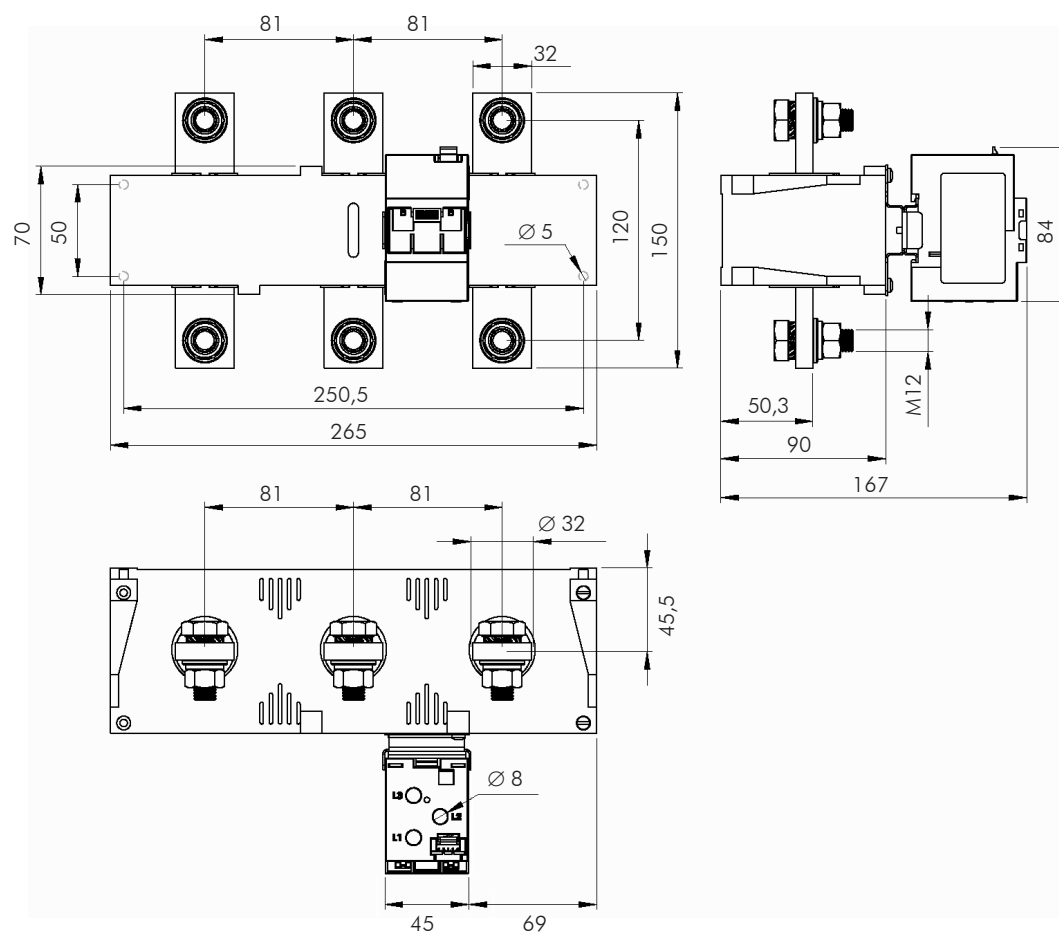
Dimensões da Unidade de Medição de Corrente – UMC 6 – Com barramento (mm)
